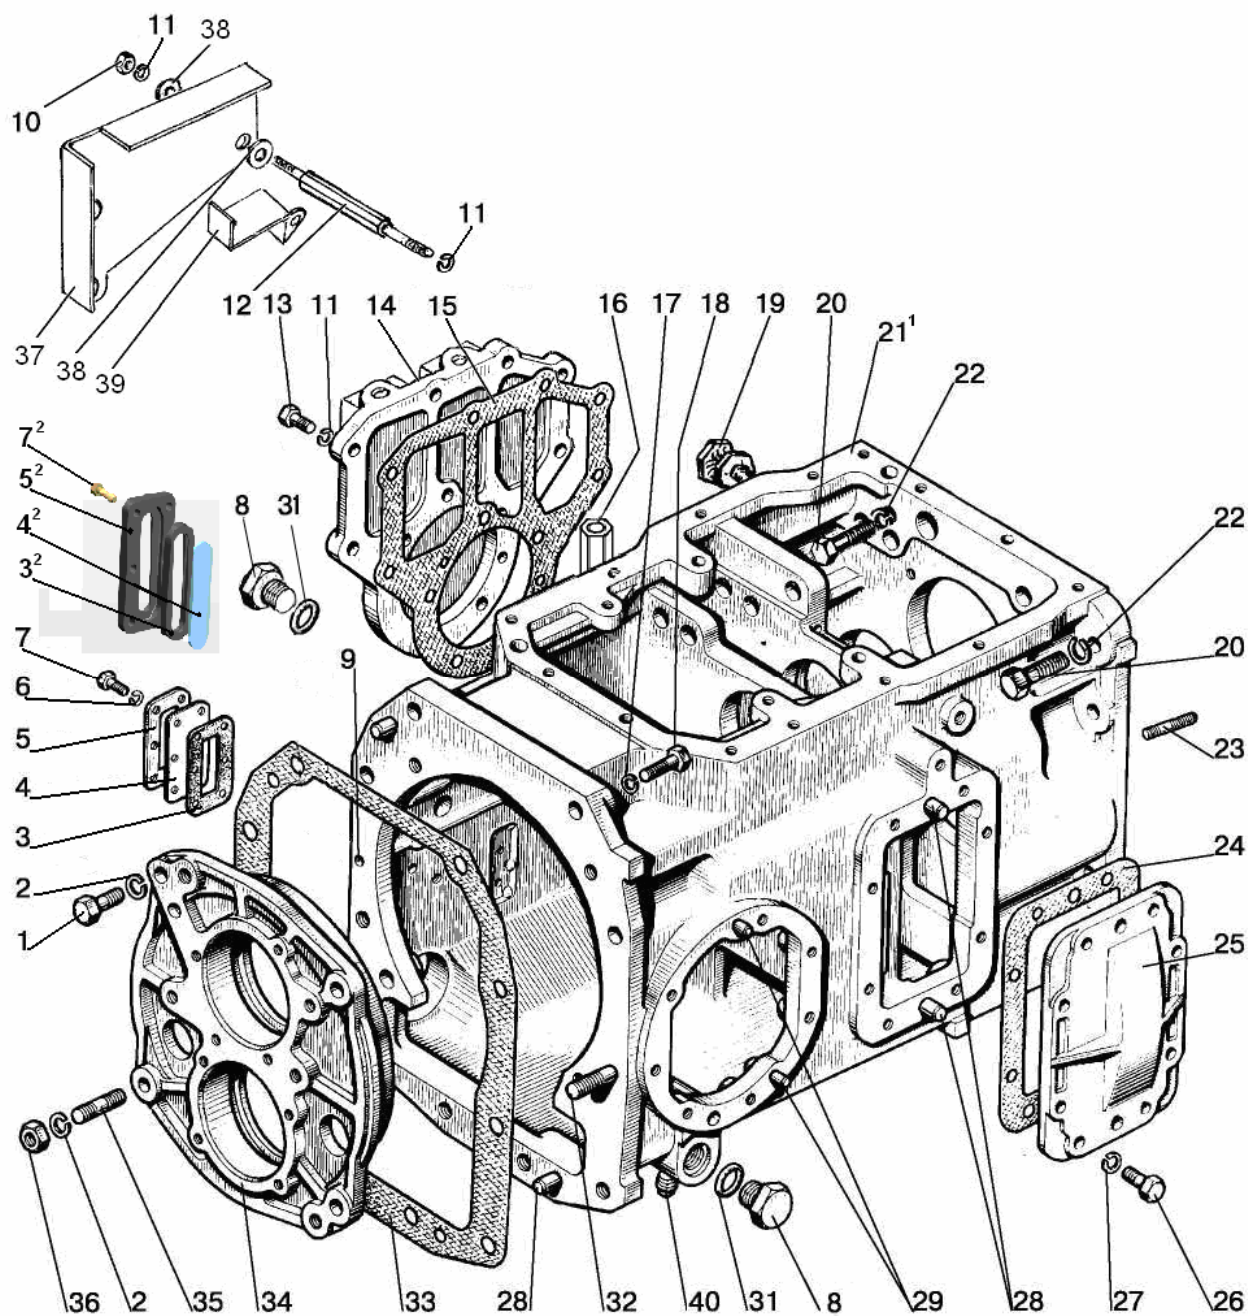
Коробка передач 112-1700010-A (16F+8R)
